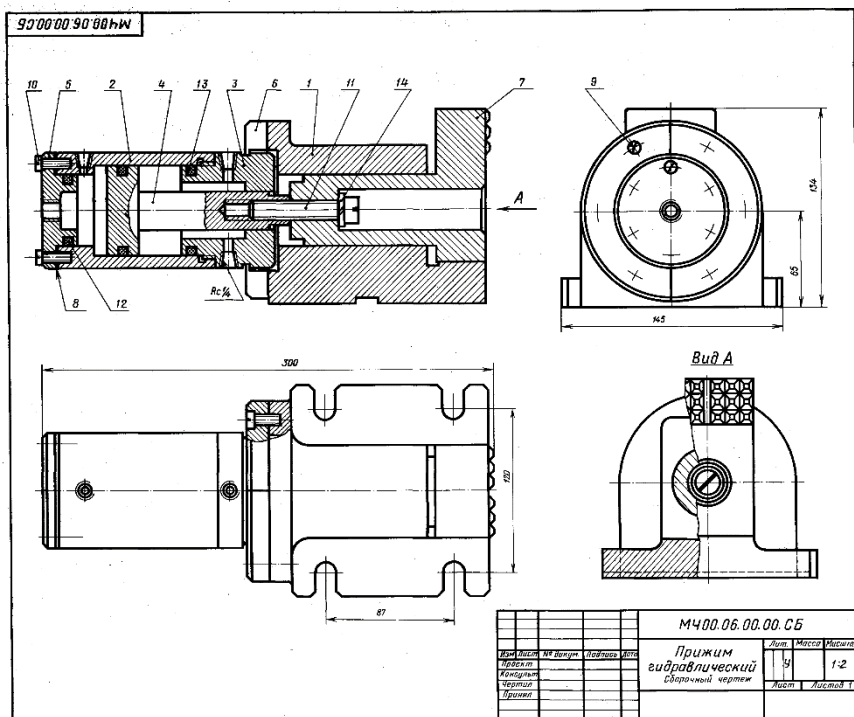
Сборочный чертеж «Прижим гидравлический»
